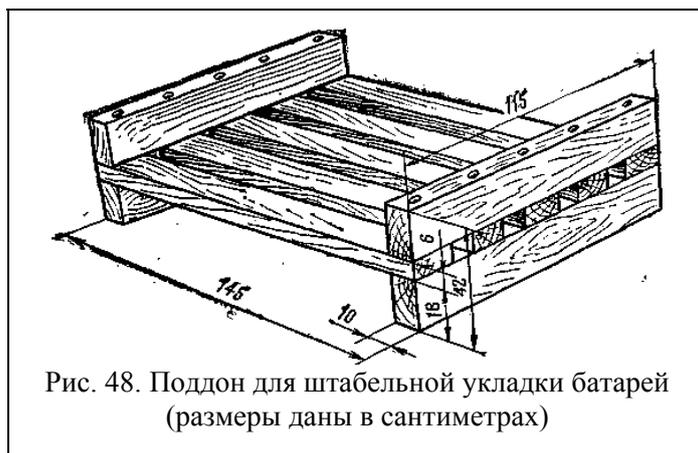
Поддон для штабельной укладки батарей (размеры даны в сантиметрах)
